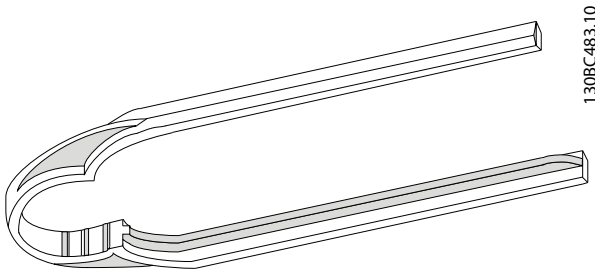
Montagewerkzeug für Kabelverschraubungen
